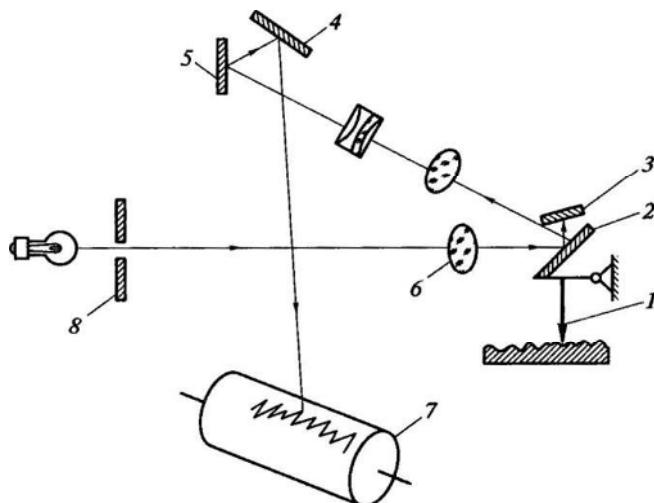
Схема оптико-механического профилографа: 1 — алмазная игла; 2—5 — зеркала; 6 — линза; 7 — барабан; 8 — диафрагма
